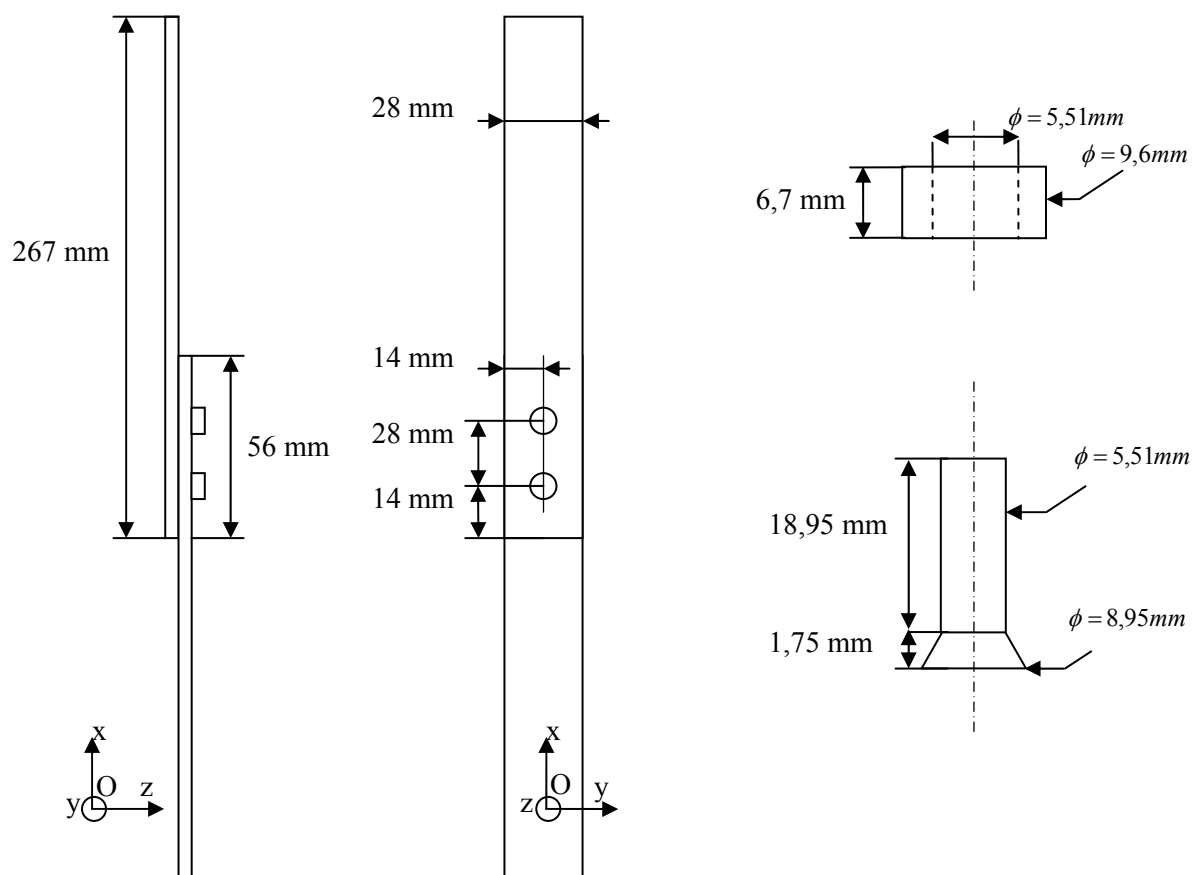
Géométrie des éprouvettes, des vis et des écrous
